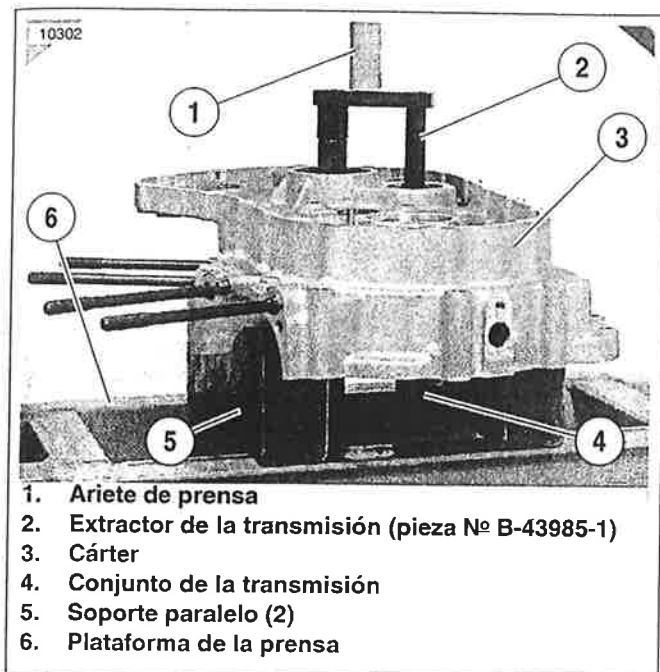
Presionar para sacar la transmisión del cárter izquierdo
